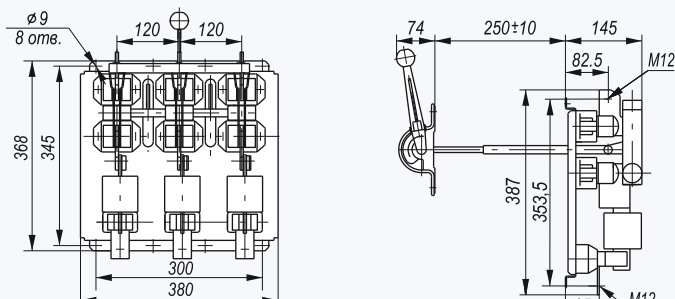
Рубильник с предохранителями на общей плате с центральным приводом РПЦ-6
